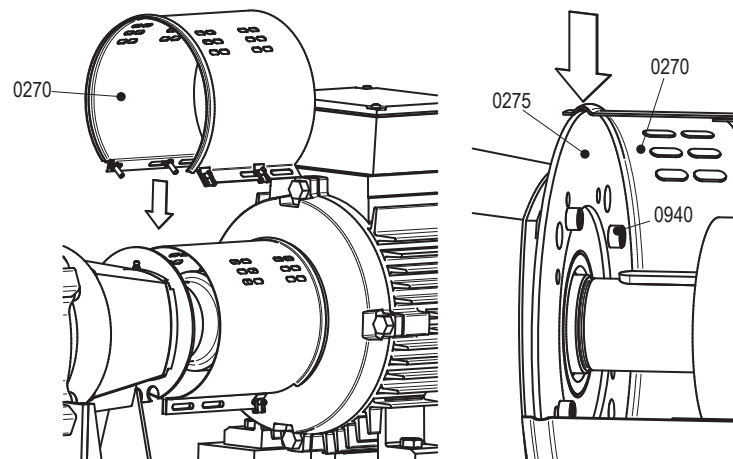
Montieren des Mantels auf der Pumpenseite.
